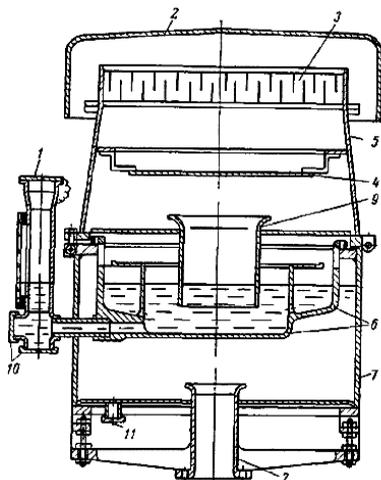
Клапан тип НКДМ: 1 – трубка для слива и налива жидкости; 2 – крышка; 3 – огневой предохранитель; 4 – экран; 5 – верхняя часть корпуса; 6 – чашка для размещения жидкости гидрозатвора; 7 – нижняя часть корпуса; 8,9 – патрубки; 9, 10 – сливные штуцеры
